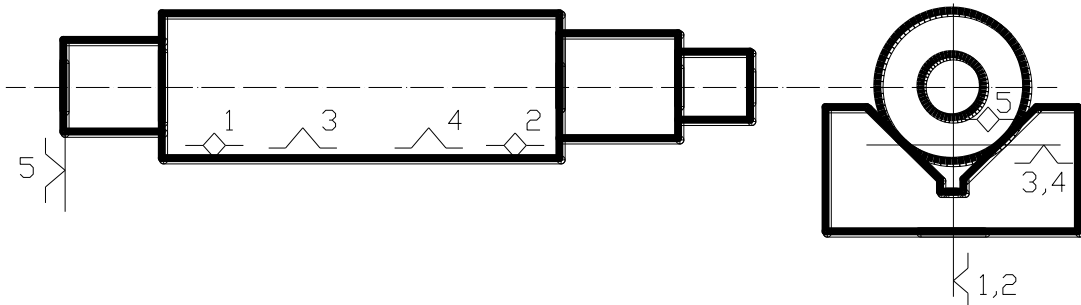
Чистові технологічні бази при свердлінні поперечних отворів та фрезеруванні шпонкових пазів (базування в призмах)
